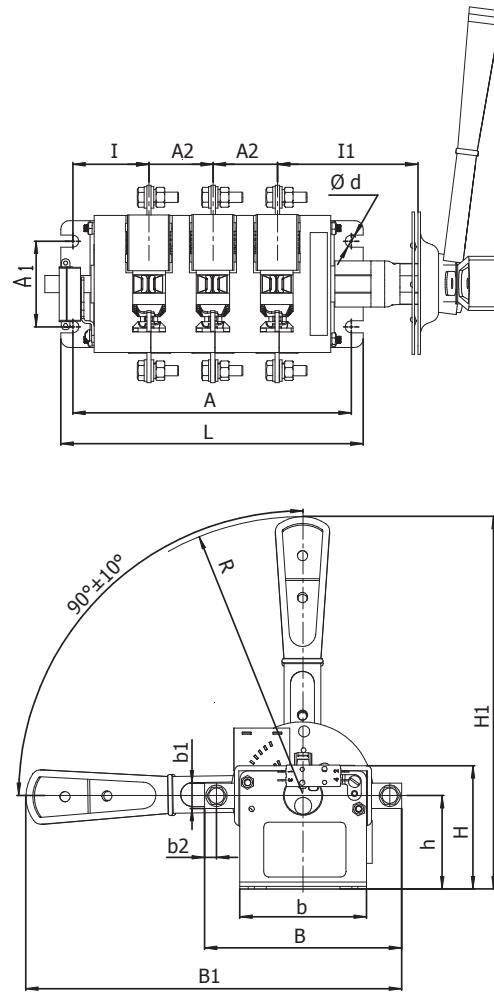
Выключатель-разъединитель трехполюсный на одно направление с боковой смещенной рукояткой.
